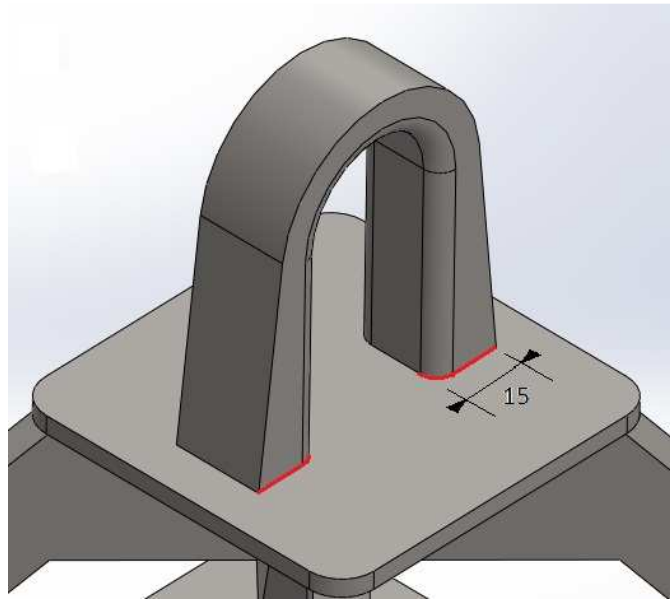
Detalhe do menor comprimento de solda na estrutura
